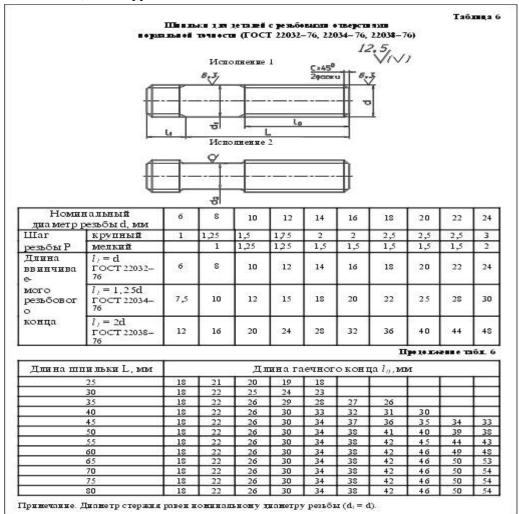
Шпилька для деталей с резьбовыми отверстиями нормальной точности
